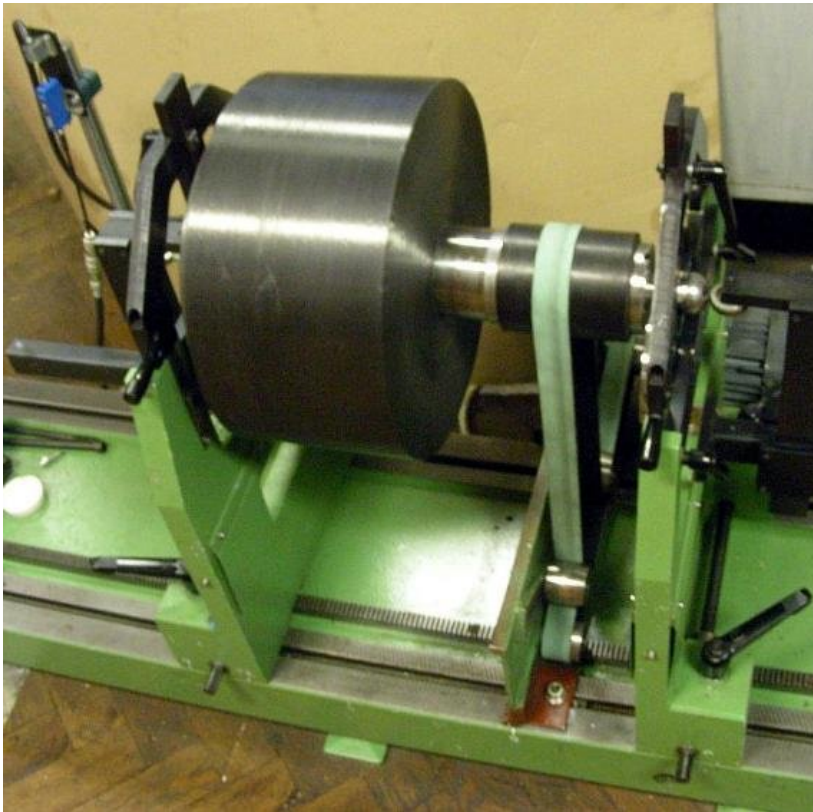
Der Rotor des Schwungrads T4 auf der Wuchtmaschine
